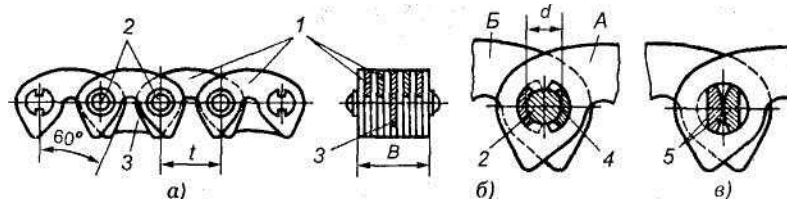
Зубчатая цепь: 1 — пластины; 2 — валики; 3 — направляющие пластины; 4 — шарнир; 5 — призмы
